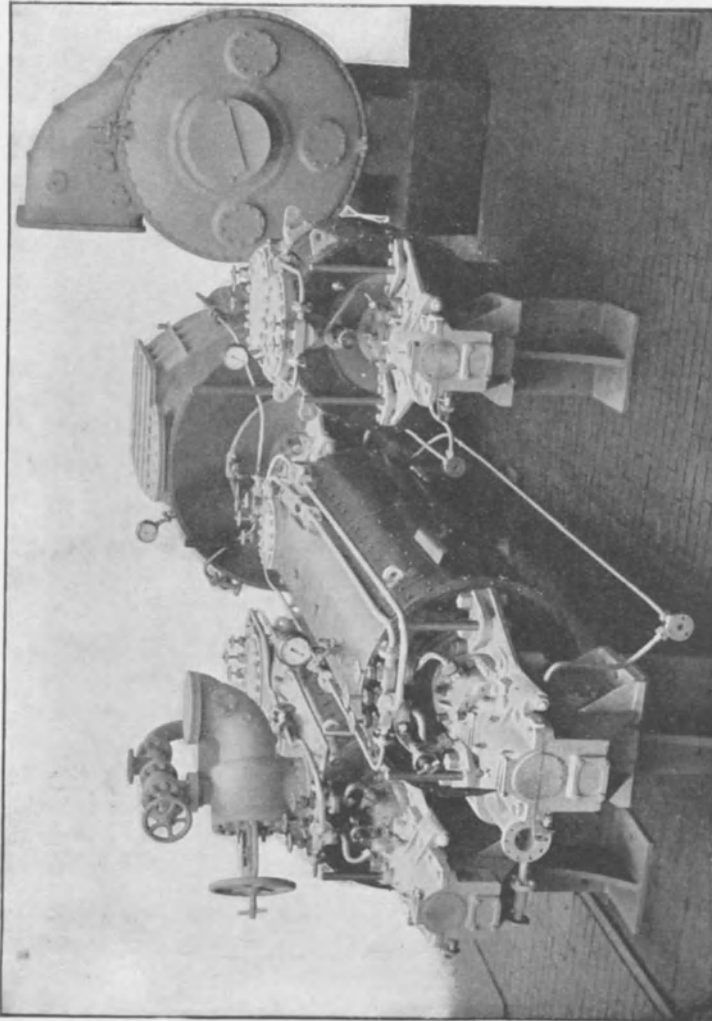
Parsonsturbinen-Anlage für ein Torpedoboot.
